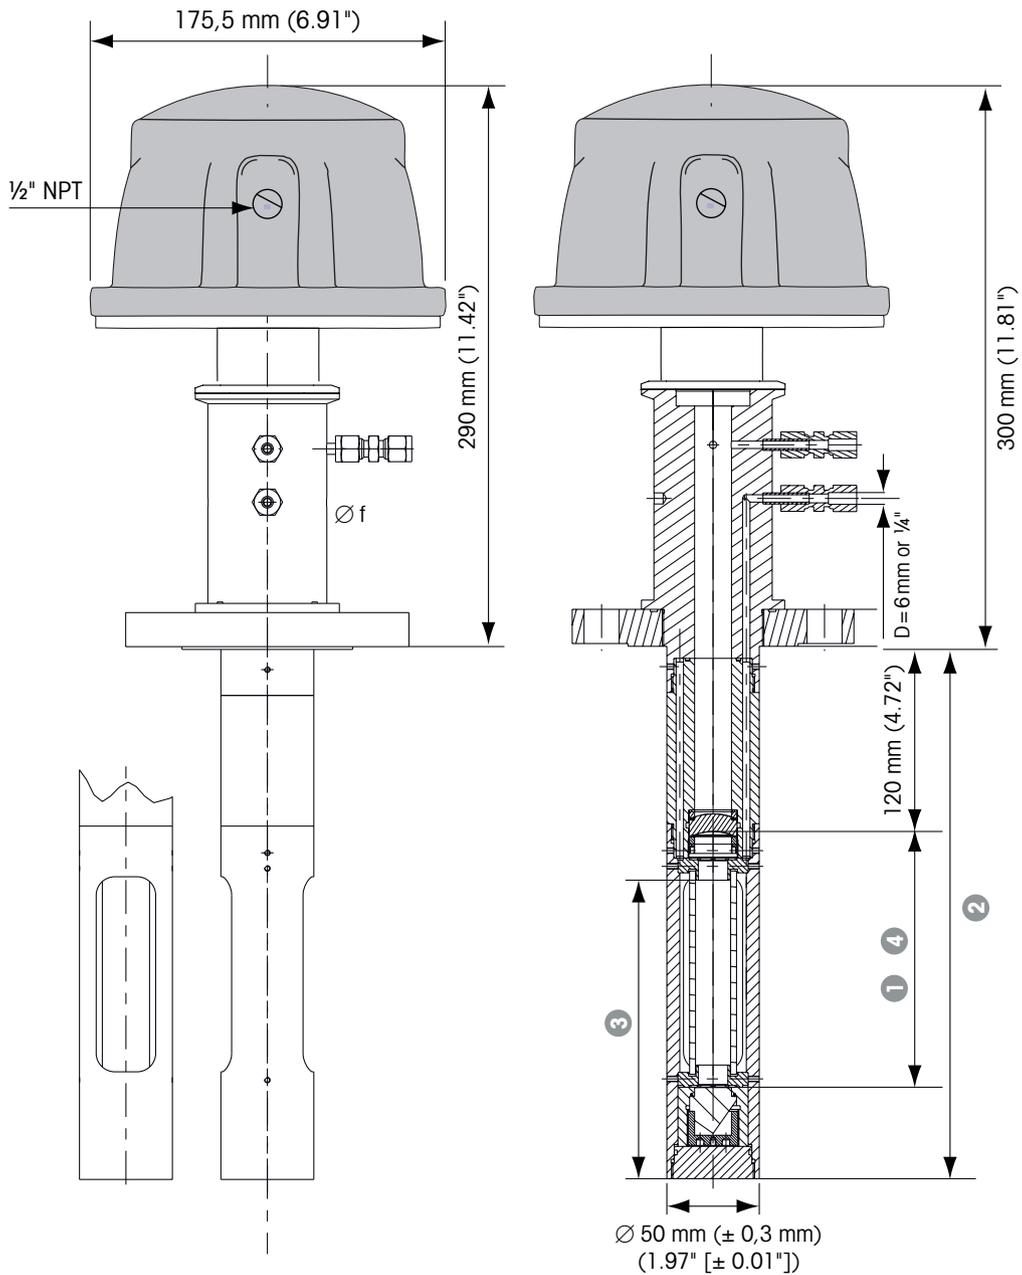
Dimensiones del sensor sin purga (B) con retroceso
